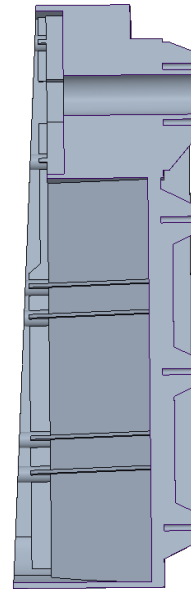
Corte de columna media con diseño vertical.
